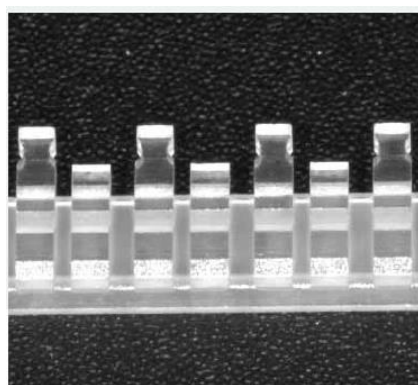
Фрезеровка паза и крыльев брекета (брекеты клыков с крючками)
